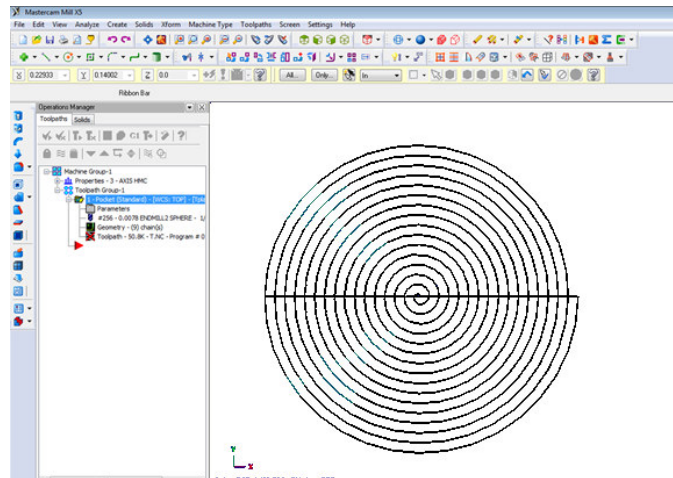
Geometría del espiral en MasterCAM para maquinado en CNC.
